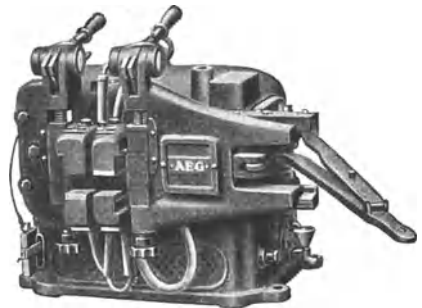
Kleine Tisch-Stumpfschweißmaschine.
